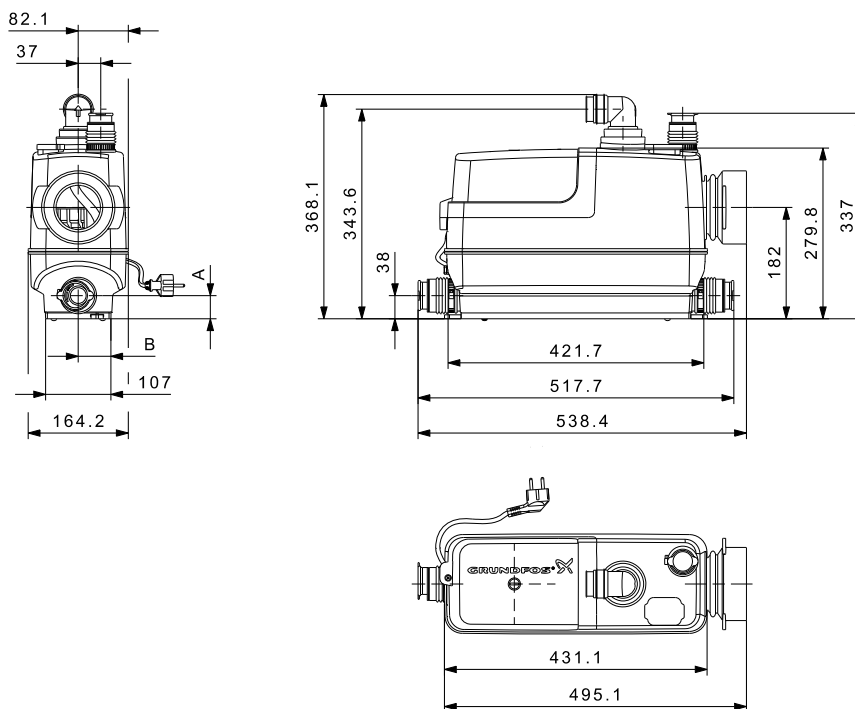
Габаритные чертежи Sololift2 CWC-3
